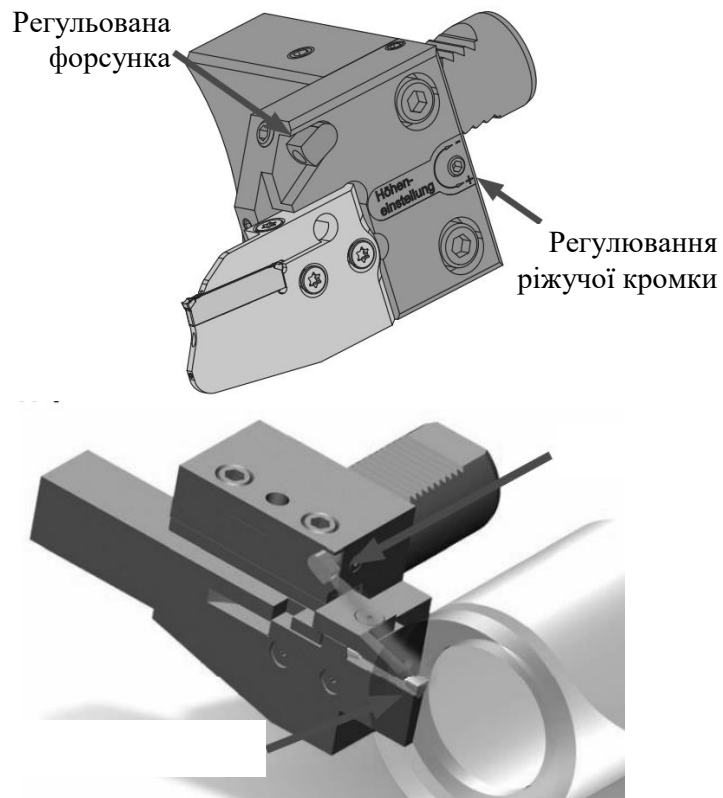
Тримач типу «Міуано» від Arno-Werkzeuge [5]
